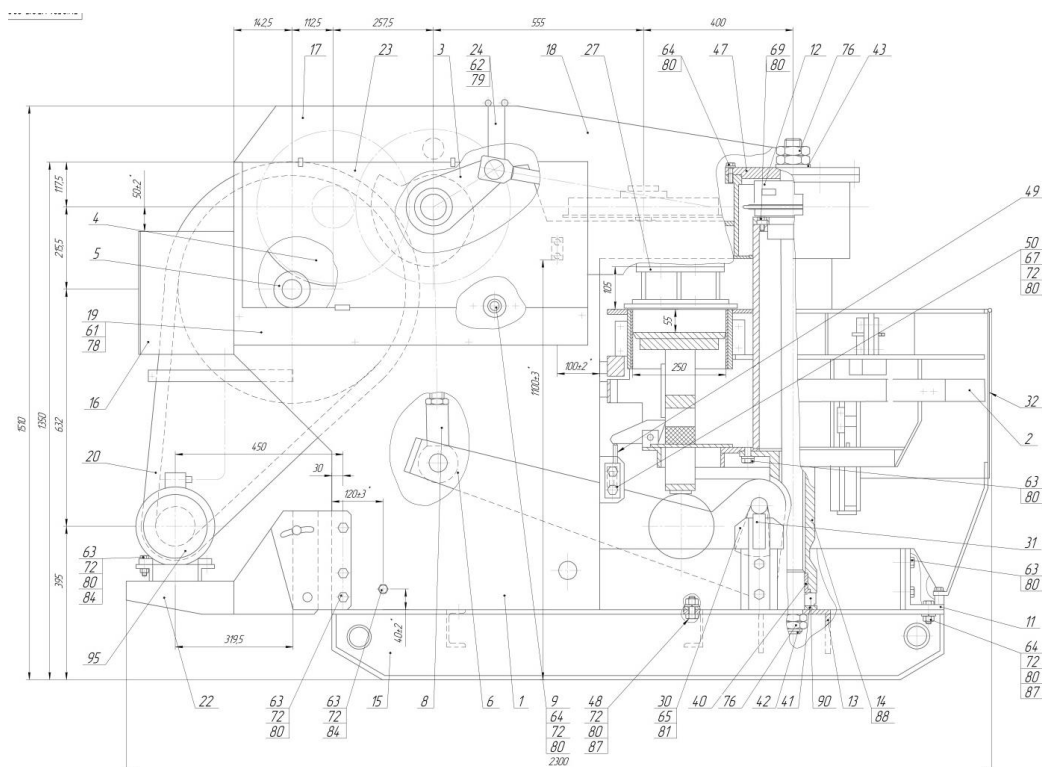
Вид загальний револьверного преса для формування напівфабрикатів керамічної цегли.
